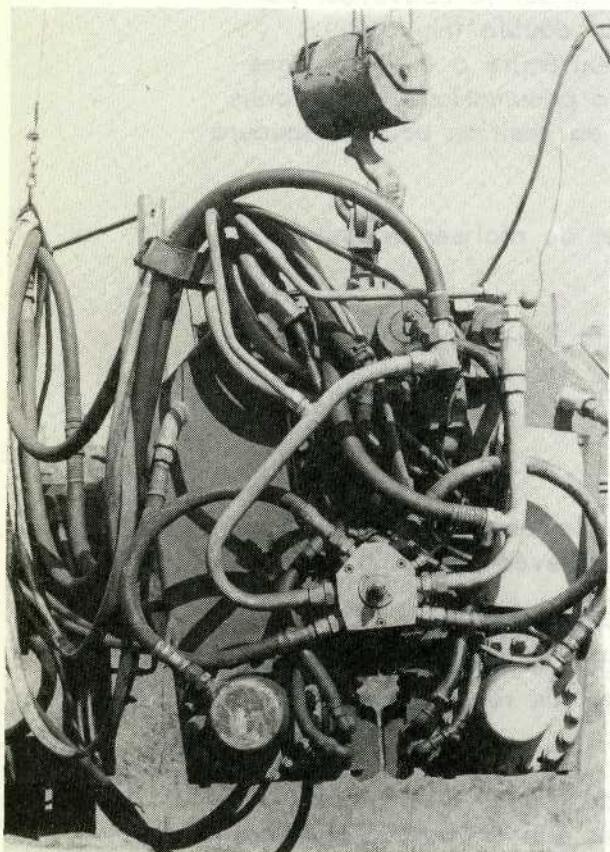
Vue de la tête de soudage qui enserre les rails à souder.
